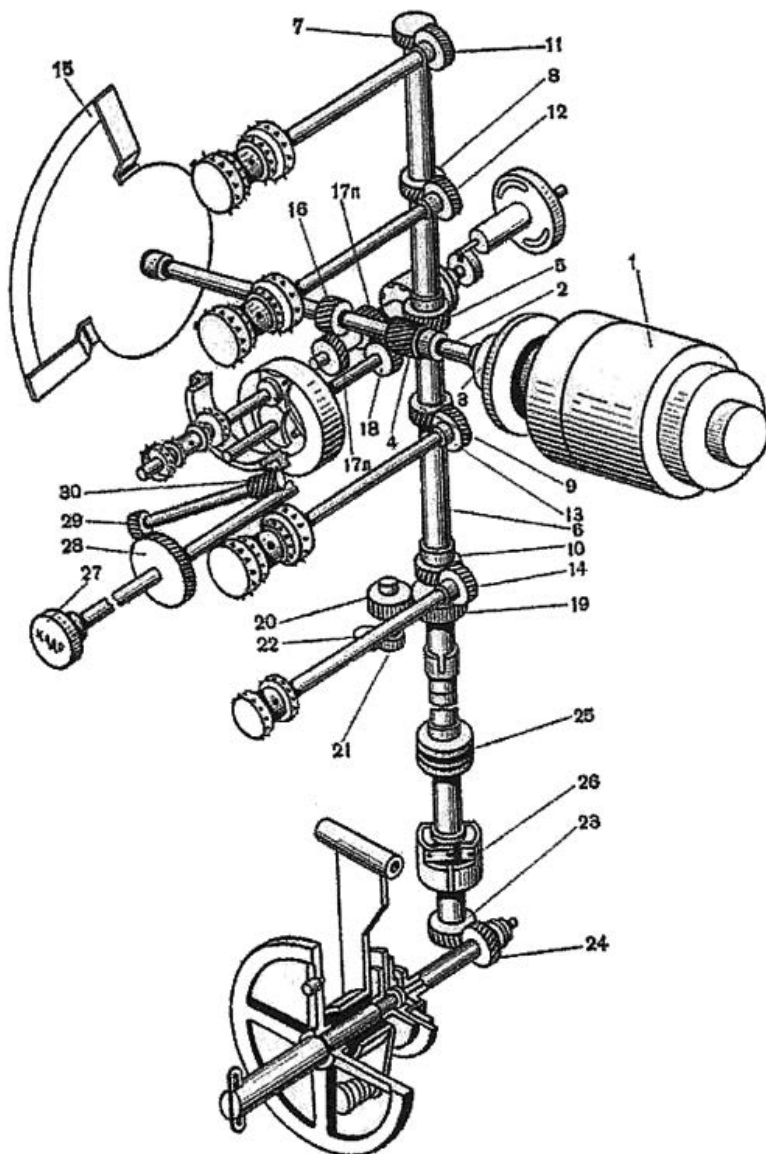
Кінематична схема приводного механізму кінопроектора КП-15:
